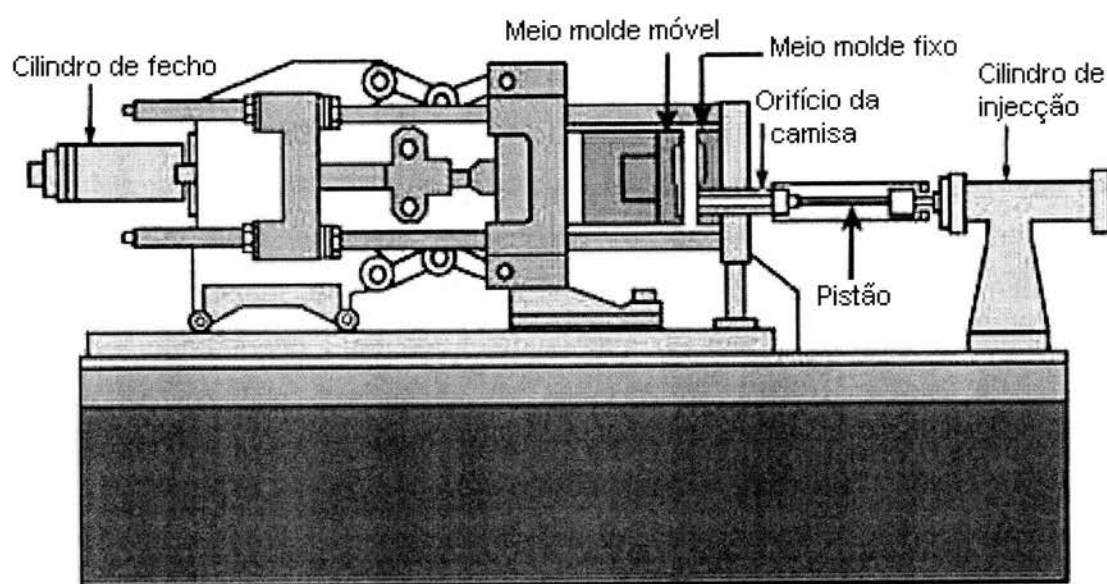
Esquema de uma máquina de Fundição Injectada
